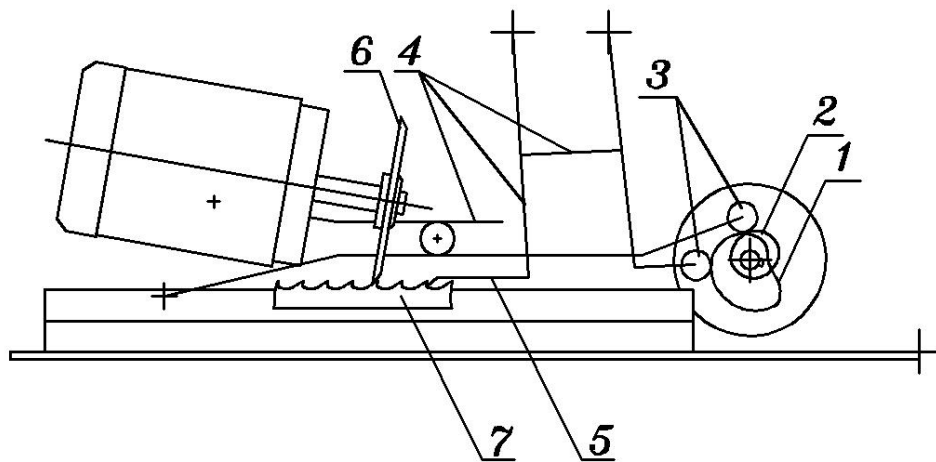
Схема двокулачкового заточувального пристрою верстату з ЧПУ 3К-327 «Тайга»
